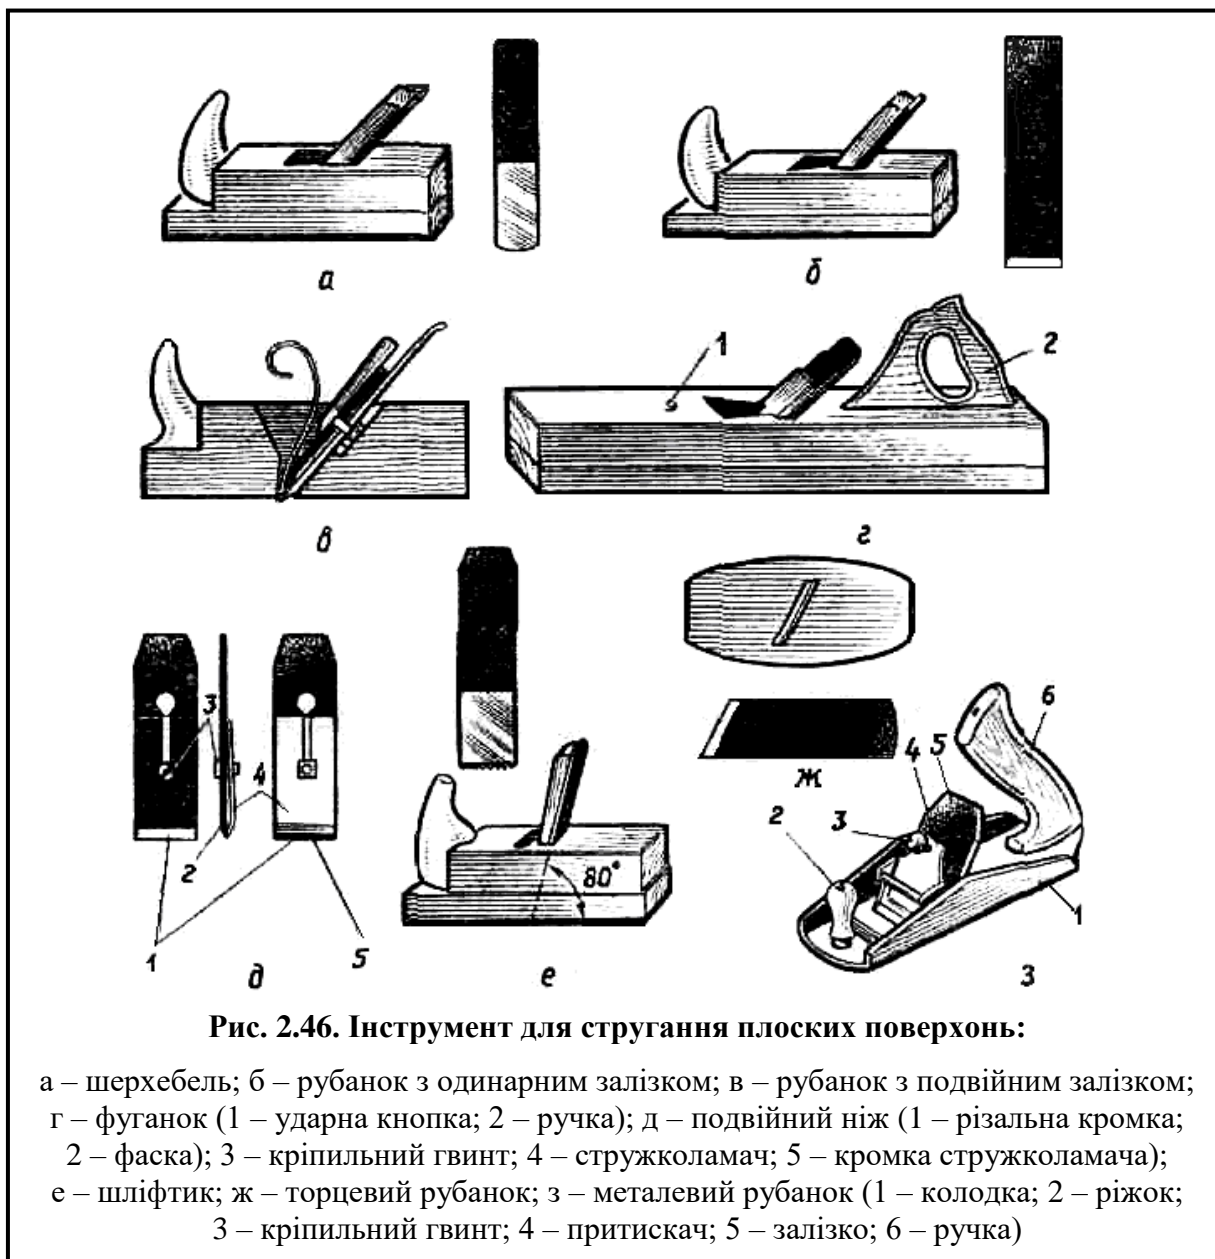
Інструмент для стругання плоских поверхнь:
